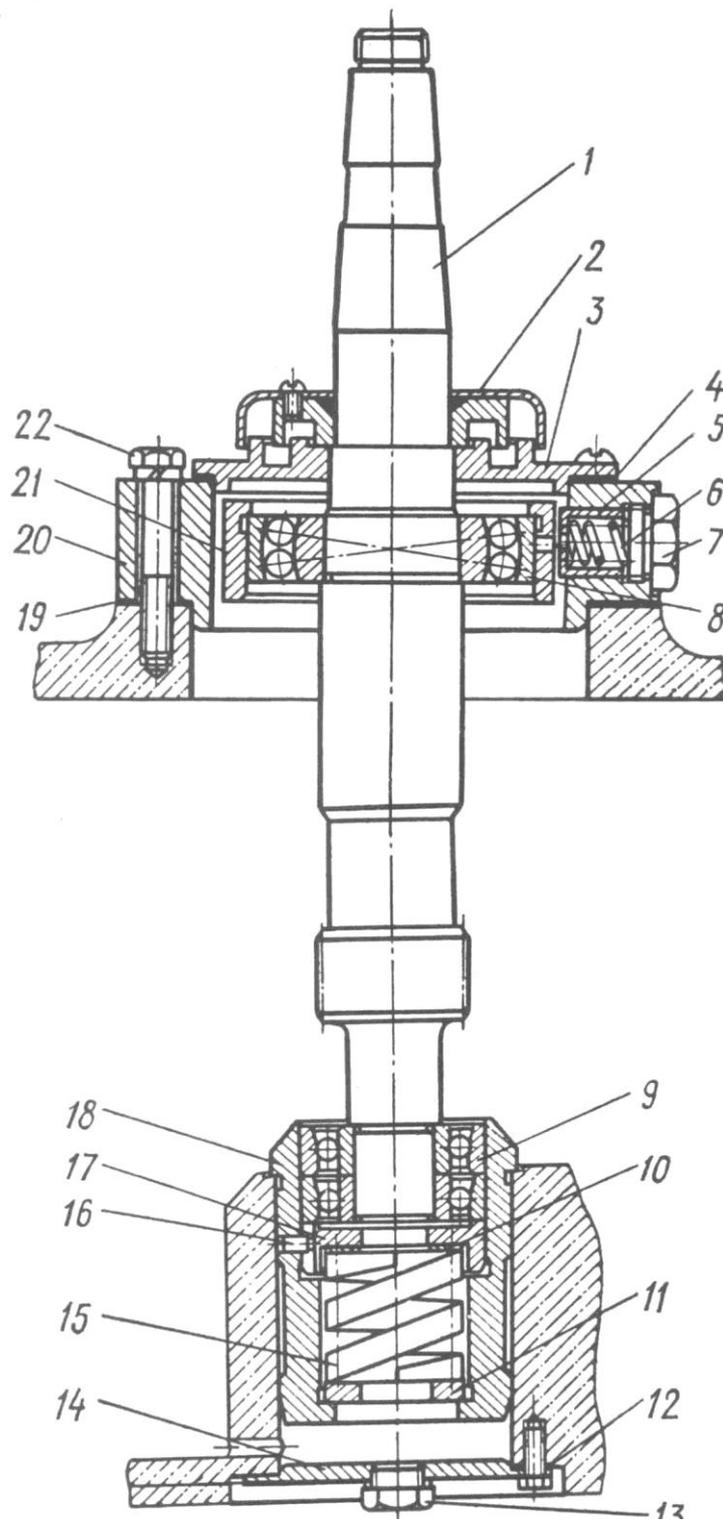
Вертикальный вал сепаратора Г9-ОСП: 1 – веретено; 2 – верхняя крышка корпуса; 4, 12, 19 – прокладки; 5 – стакан пружины; 6, 15 – пружины; 7 – резьбовая пробка; 8, 9 – шарикоподшипники; 10, 11 – упорные шайбы; 13 – пробка; 14 – крышка; 16 – штифт; 17 – упор; 18 – стакан; 20 – корпус; 21 – обойма; 22 – болт
